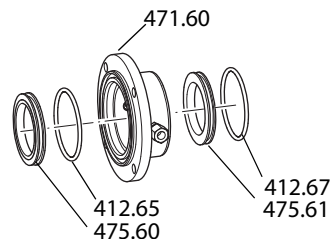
montaje previo de la carcasa del cierre mecánico, aplicación H
